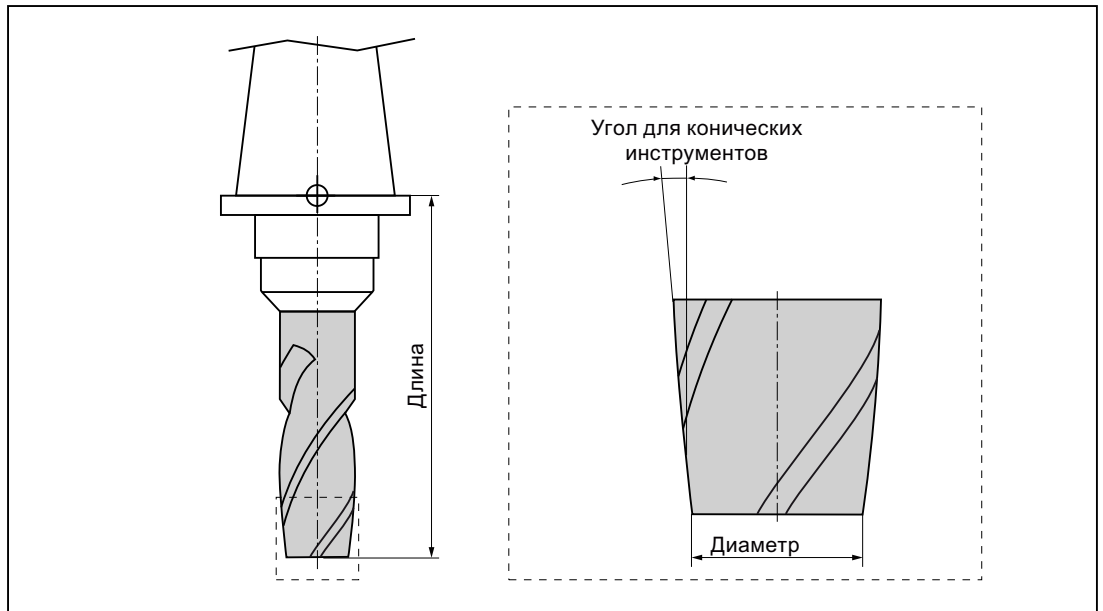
Тип инструмента 3D на примере конической фрезы (тип 155)
